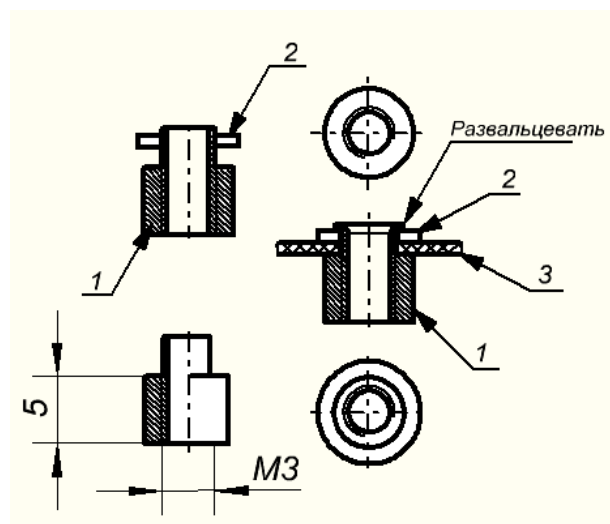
Схема втулки резьбовой для крепления печатной плате и ее монтаж на плате
